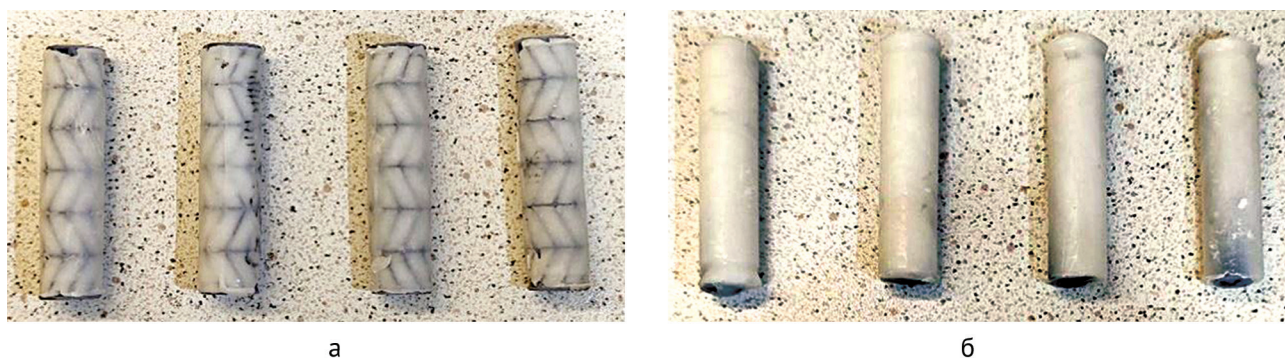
Внешний вид изготовленных образцов (а — образцы I, б — образцы II)
